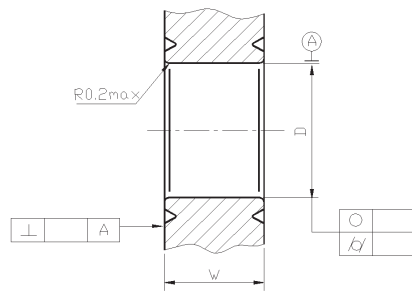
外圈倒角类型关节轴承轴承座孔的形位公差
